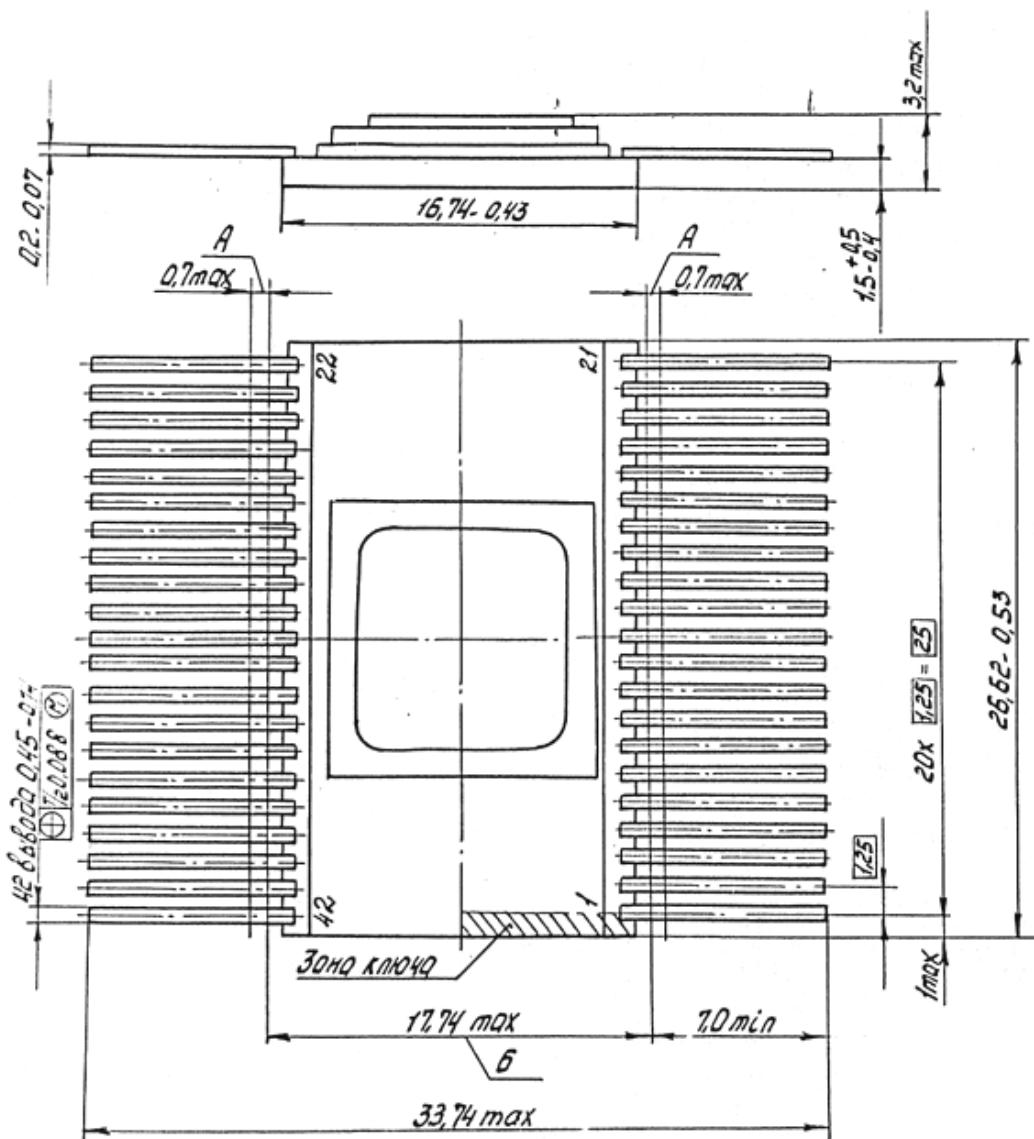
Габаритный чертеж корпуса H14.42-1В
